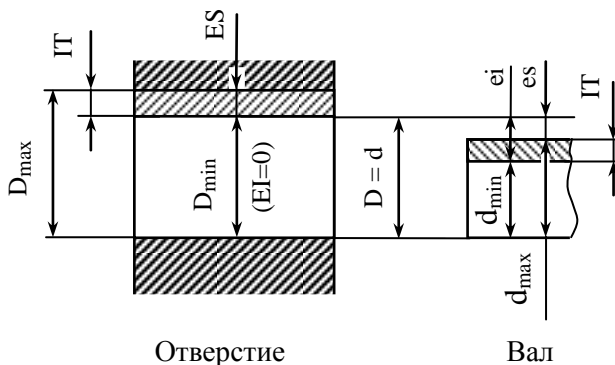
Предельные размеры отверстия и вала, определяющие поля допусков и посадку (посадка с зазором)
